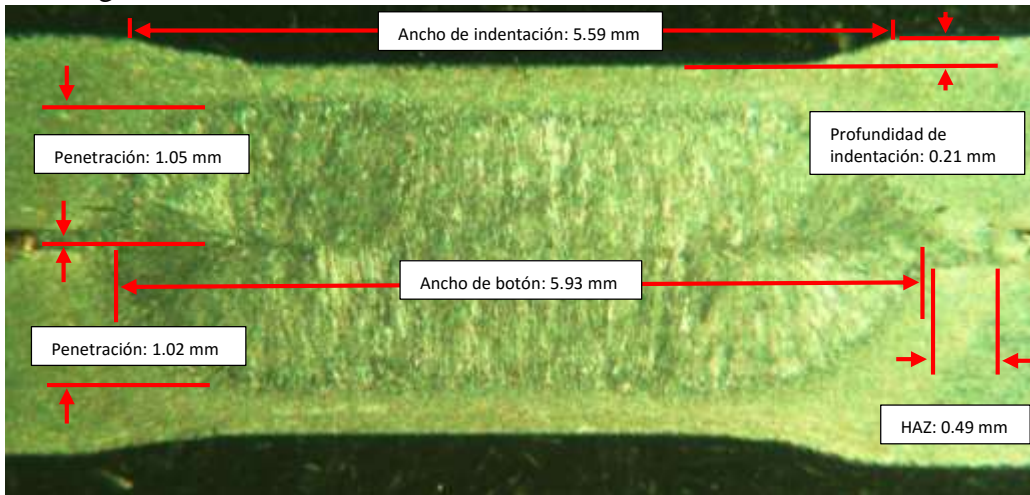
Mediciones realizadas en el botón de soldadura número 18.
